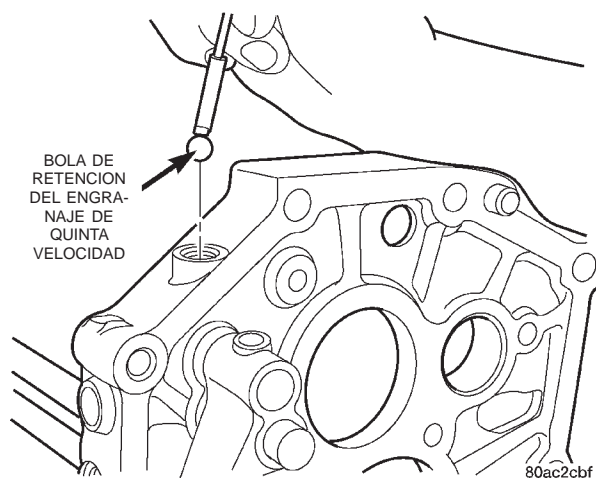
Desmontaje de bola de retención del engranaje de quinta velocidad
